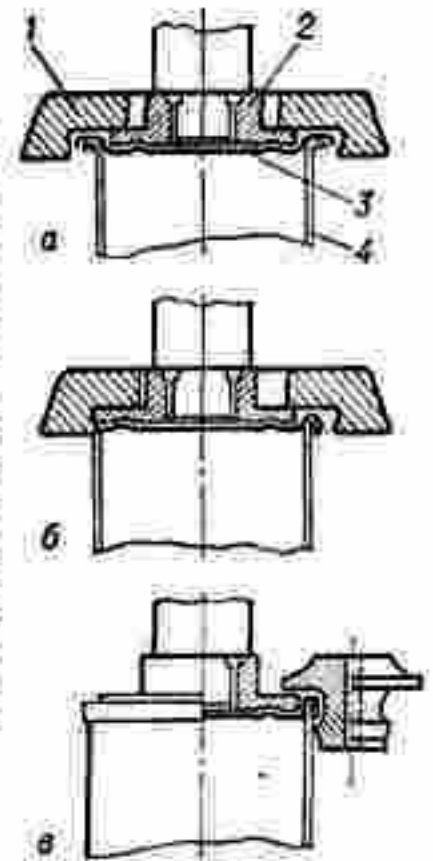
Схемы установки закаточных роликов: а — ролик 1, вращаясь и перемещаясь горизонтально к верхнему патрону 2, в к-ром зажаты банка и крышка 3, осуществляет формовку шва; б — закаточный ролик заканчивает формовку закаточного шва, образуя пять слоёв жести: три — от крышки и два — от корпуса; в — ролик плотно сжимает пять слоёв жести и уплотнительную плёнку пасты.
